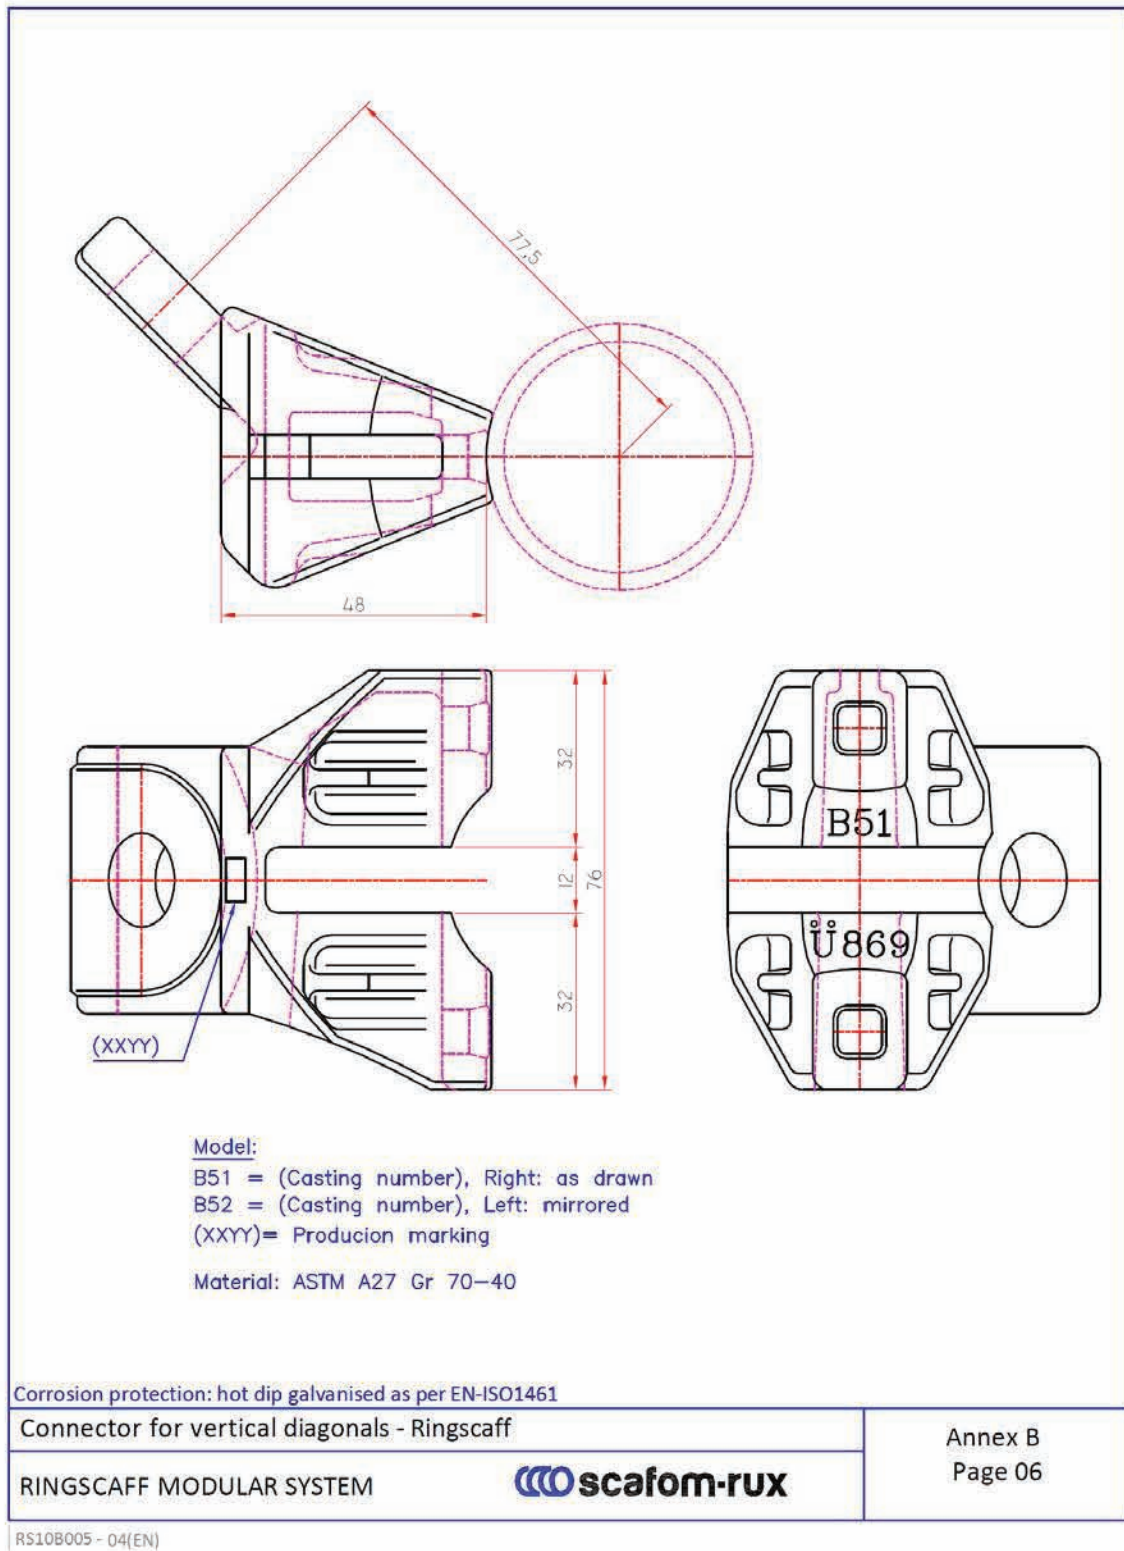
Peça de ligação dos contraventamentos verticais
